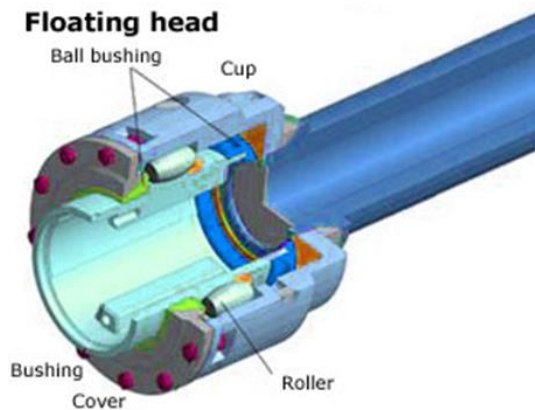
Конструкція шарніру з сферичними роликами
